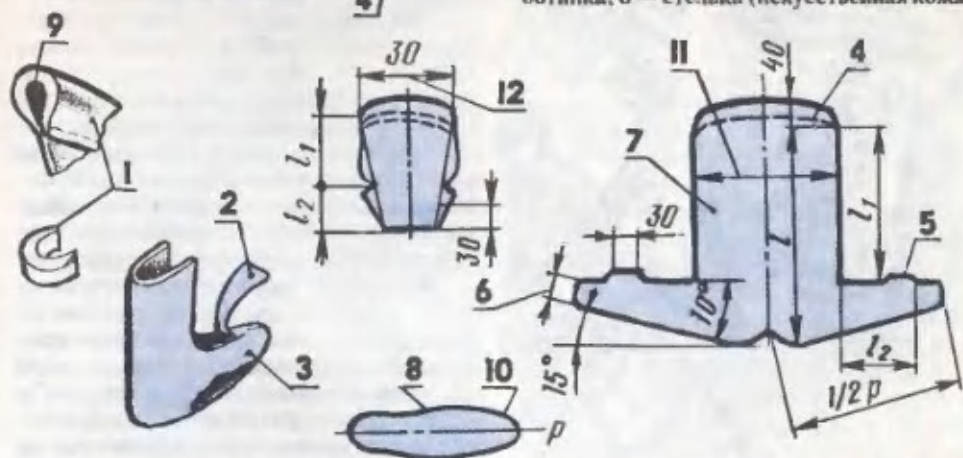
В в е р х у: шарнир. В н и з у: 1 — валик; 2 — язык и его выкройка; 3 — внутренний ботинок; 4 — линия подшивки валика; 5 — место крепления языка; 6 — высота подъема; 7 — выкройка внутреннего ботинка; 8 — стелька (искусственная кожа),
